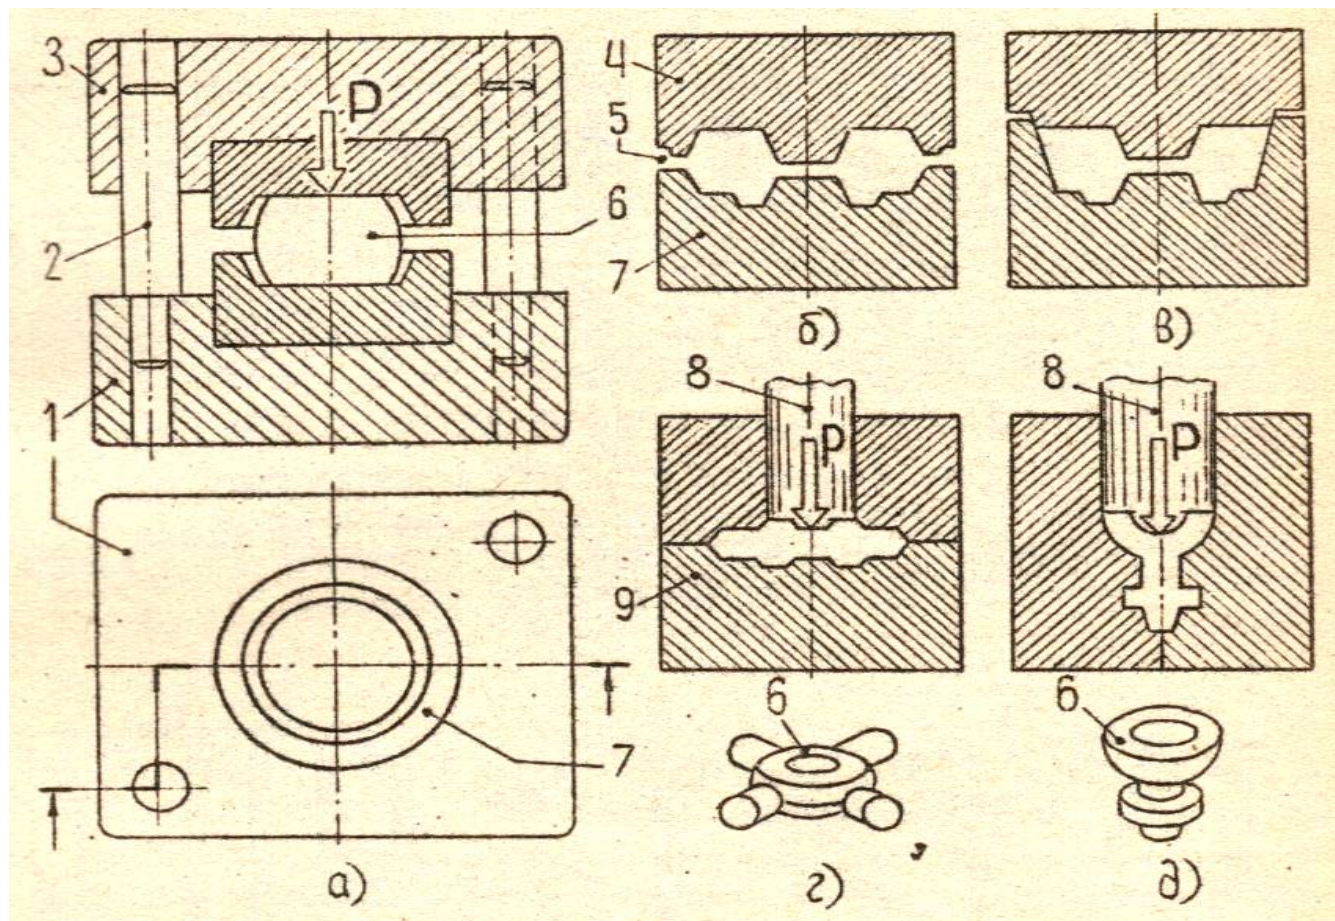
Схема штампа для КГШП и конструкции вставок:
